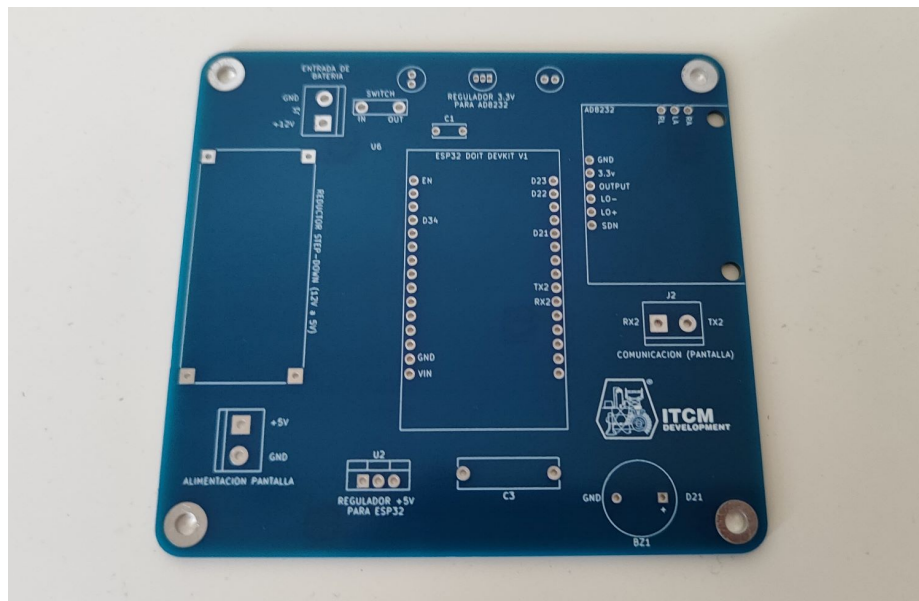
PCB profesional previo a soldadura de componentes
